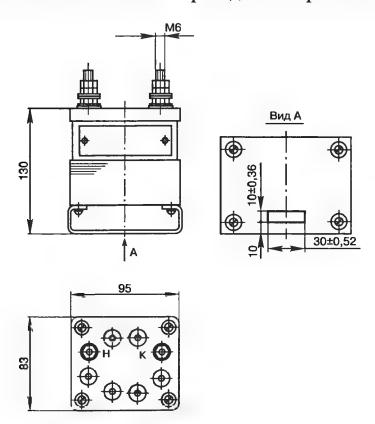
Присоединительные и габаритные размеры реакторов РОБС-1A, РОБС-3A и РОБС-4A
